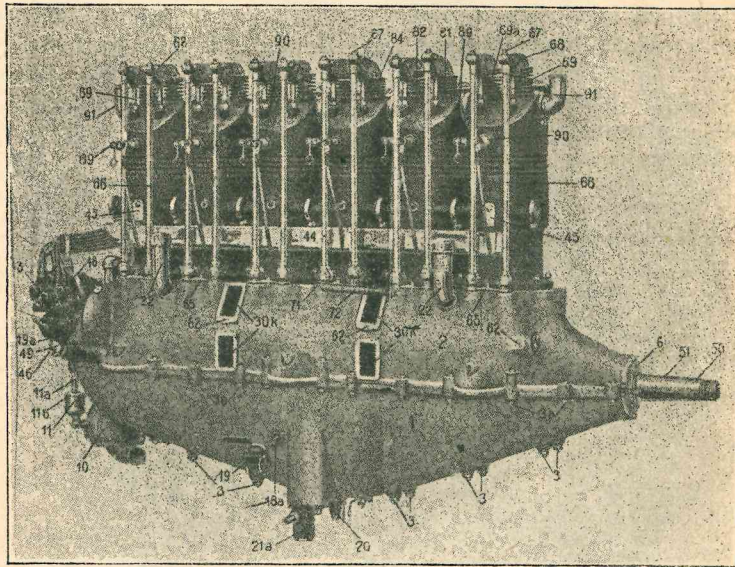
150-сильный двигатель „Бенц“ (вид со стороны клапанного устройства).
